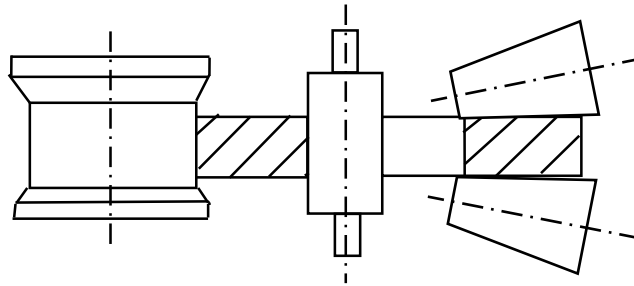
Валки робочої кліті стану для прокатки кілець
